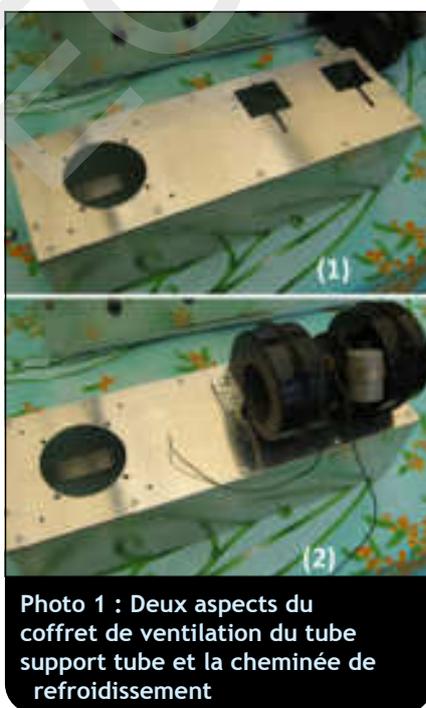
Deux aspects du coffret de ventilation du tube support tube et la cheminée de refroidissement
